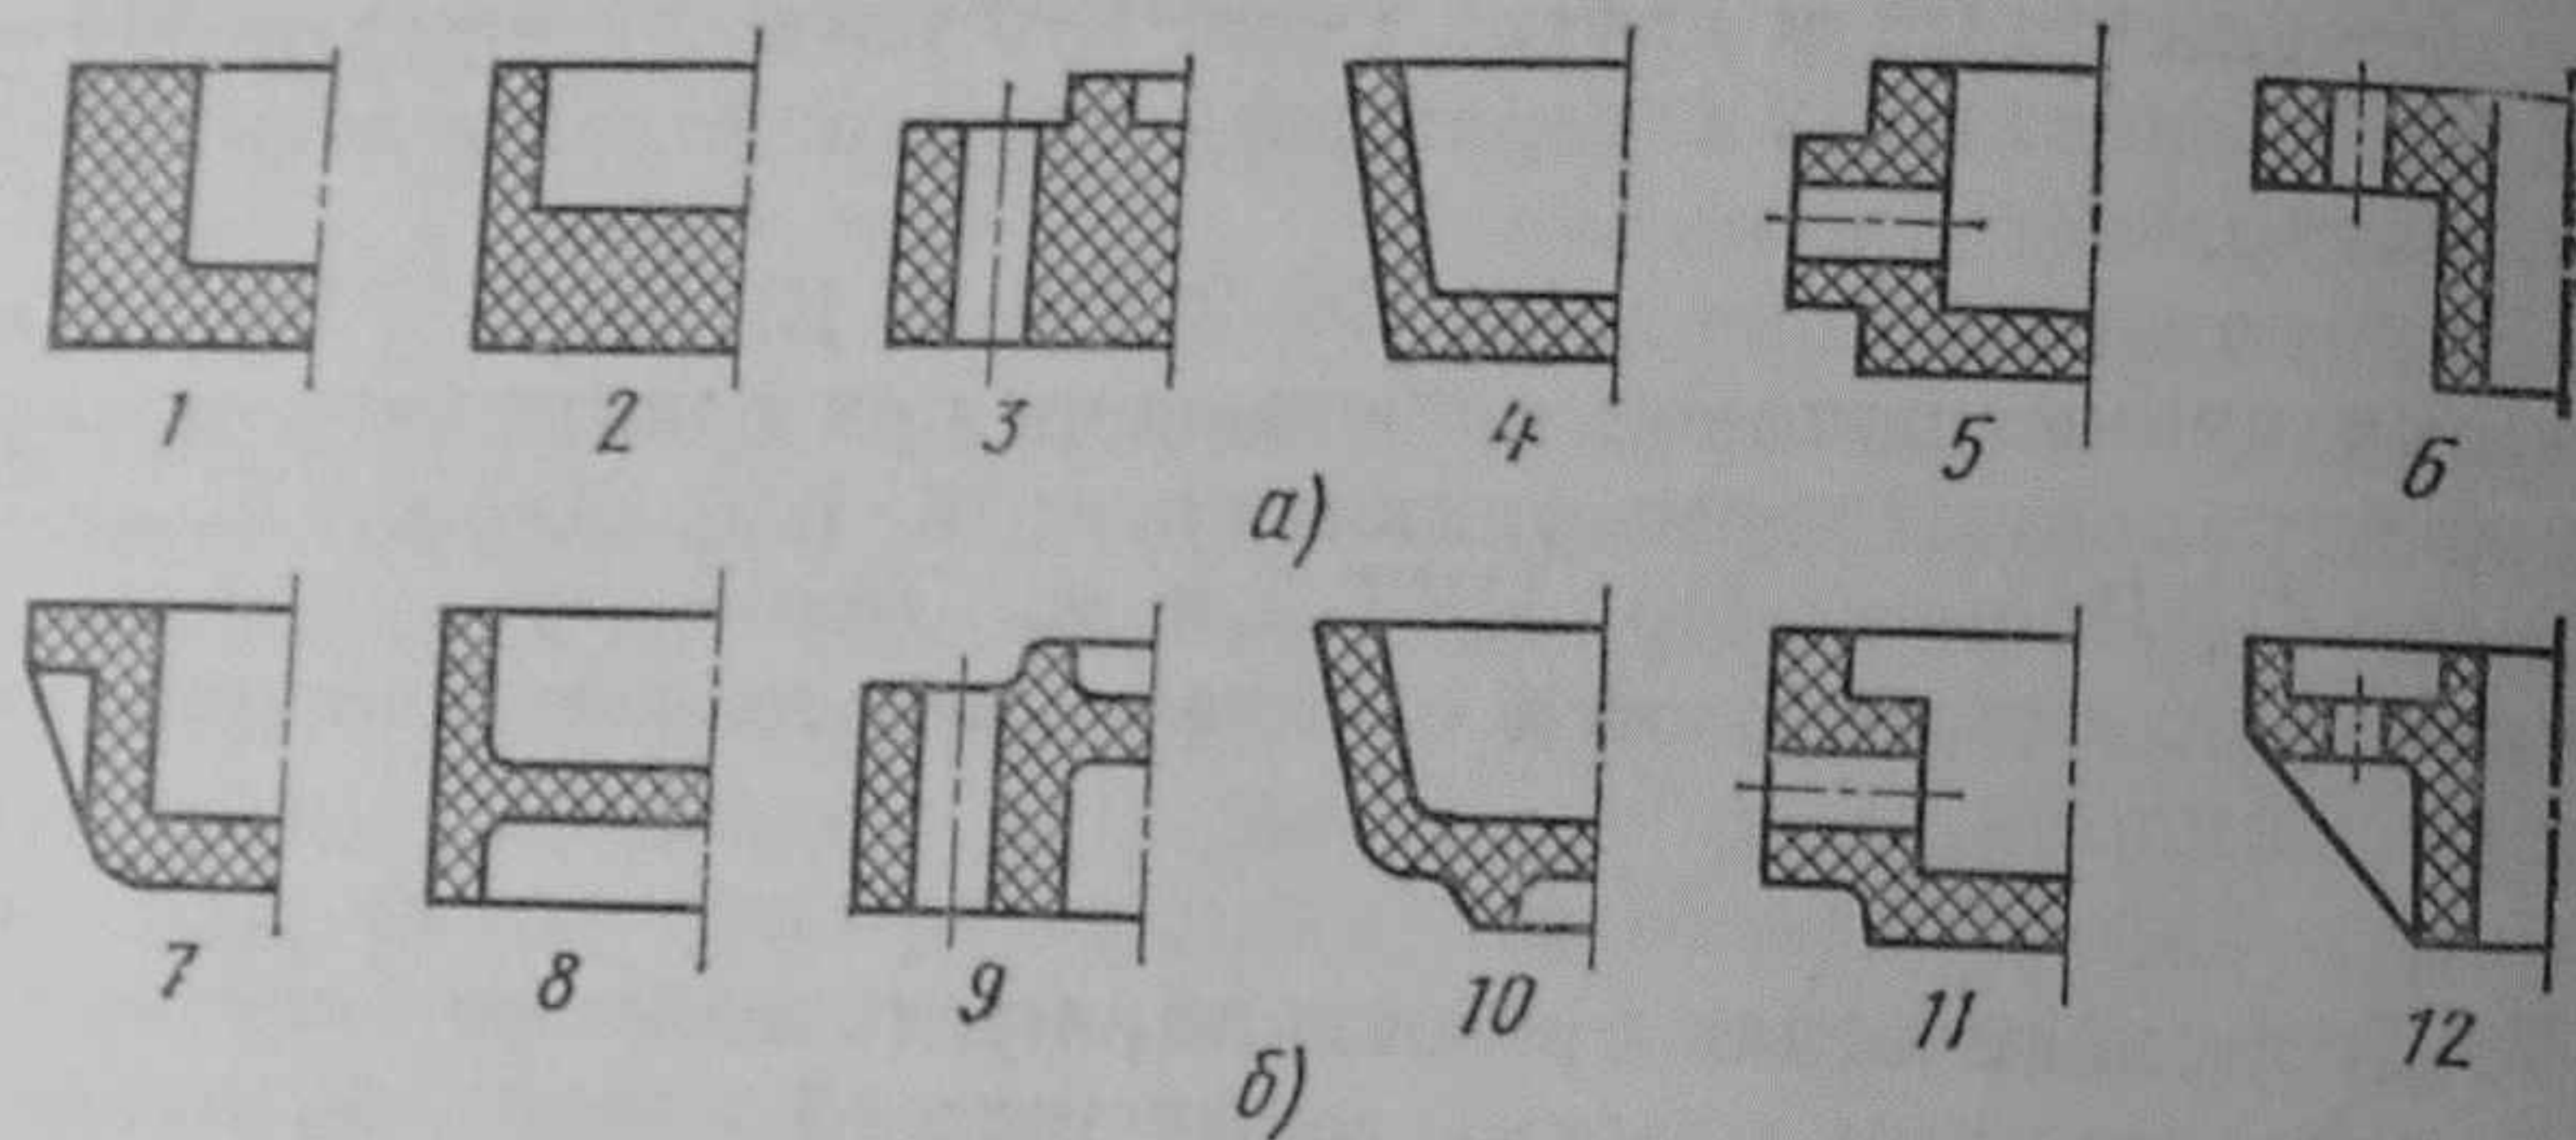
Примеры конструктивного оформления пластмассовых деталей:
